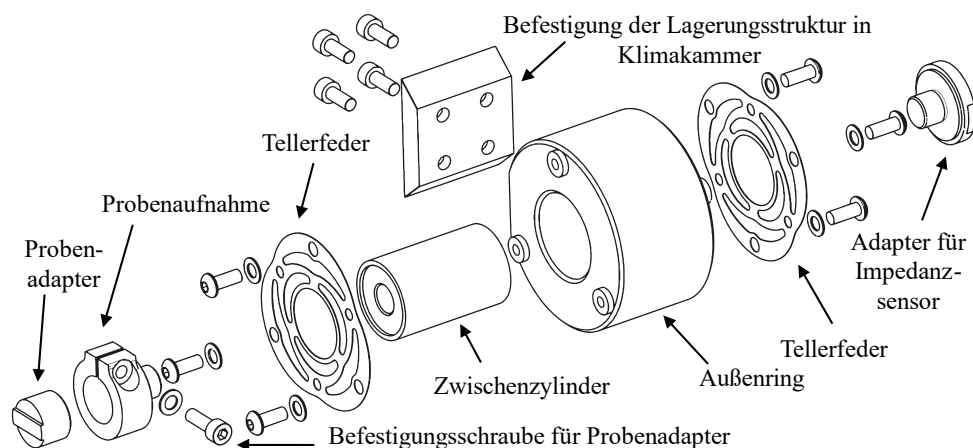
Explosionszeichnung der Lagerungsstruktur [UA19] [UAM21]
